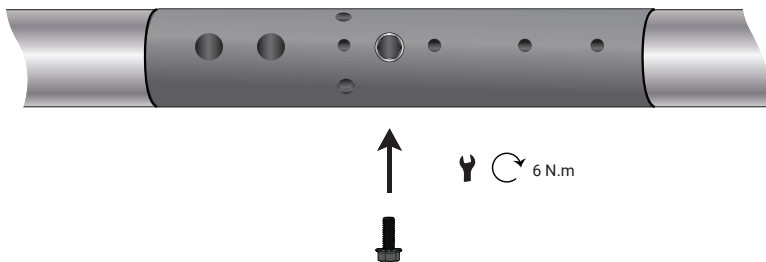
Opnieuw gemonteerde bevestigingsbout voor de inwendige equipotentiaalverbinding
